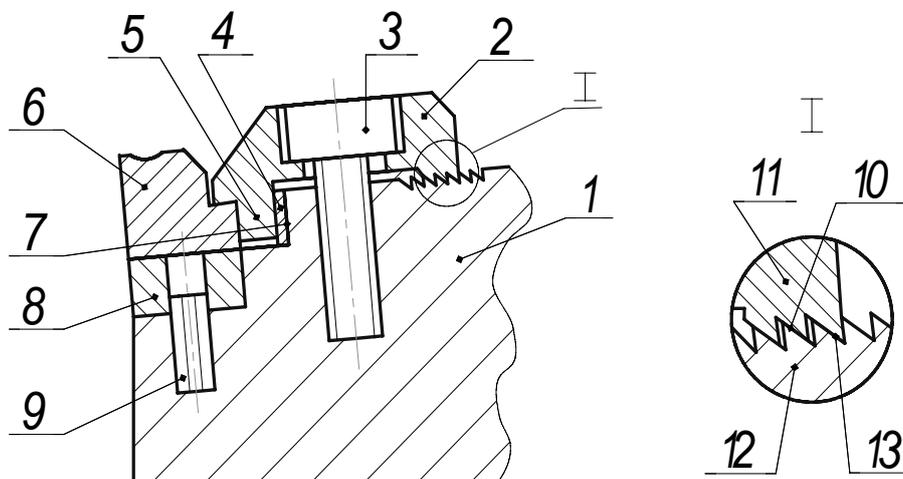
Сборный резец по авторскому свидетельству № 1144784 (конструкция 1)
